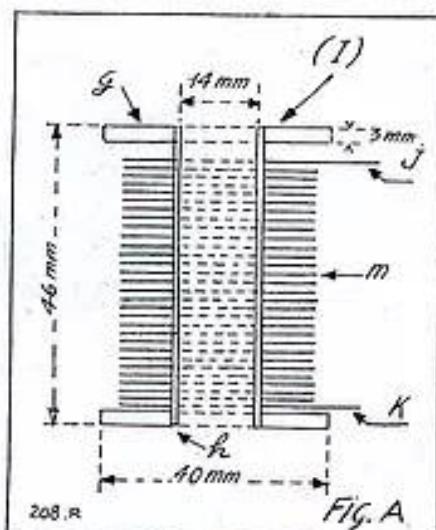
Détails de la bobine d'électro-aimant, sans noyau magnétique. — h : corps de la bobine. — g : joues de la bobine. — m : bobinage. — j : entrée du bobinage. — k : sortie du bobinage.
